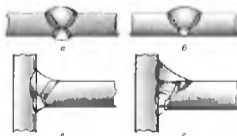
Сварные соединения с подварочным швом а — двусторонний стыковой с двумя симметричными скосами кромок, б — односторонний стыковой со скосом двух кромок, в — тавровый со скосом кромок двусторонний, г — тавровый со скосом кромок многопроходный
